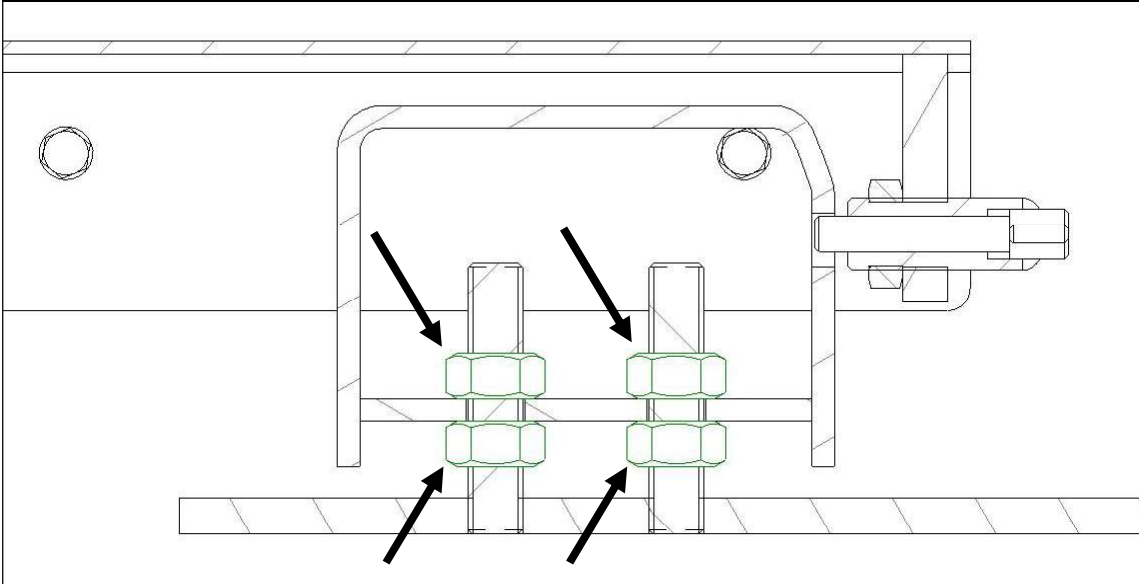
Écrous à manipuler pour le réglage du châssis.
